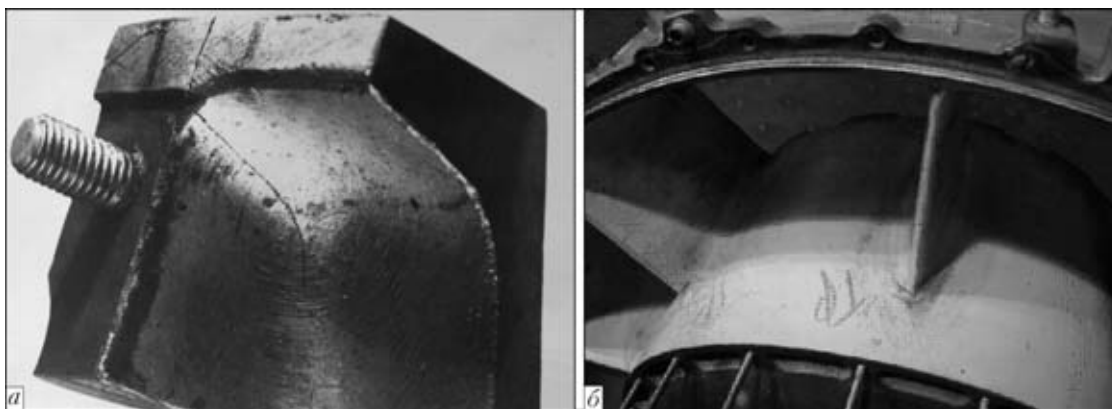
Вид трещин на поверхности отливок из сплава Мл-10: а — фрагмент лобового картера; б — корпусная деталь
